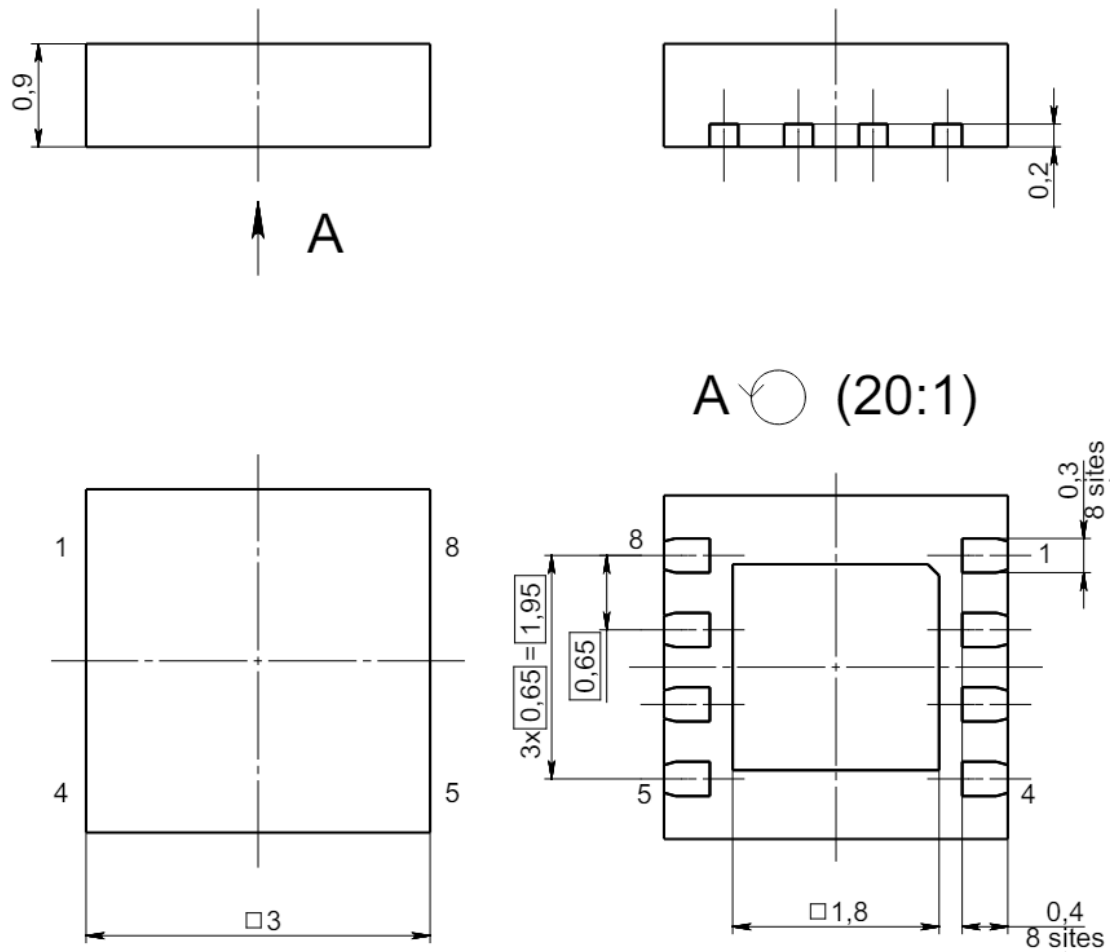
Габаритный чертеж корпуса DFN300X300X90-8 (размеры в мм)
